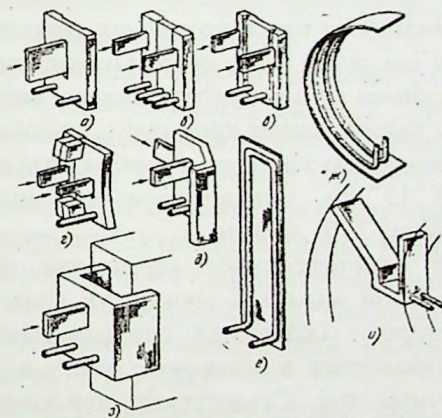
Подвижные и неподвижные формирующие устройства для электрошлаковой сварки (ползуны):
